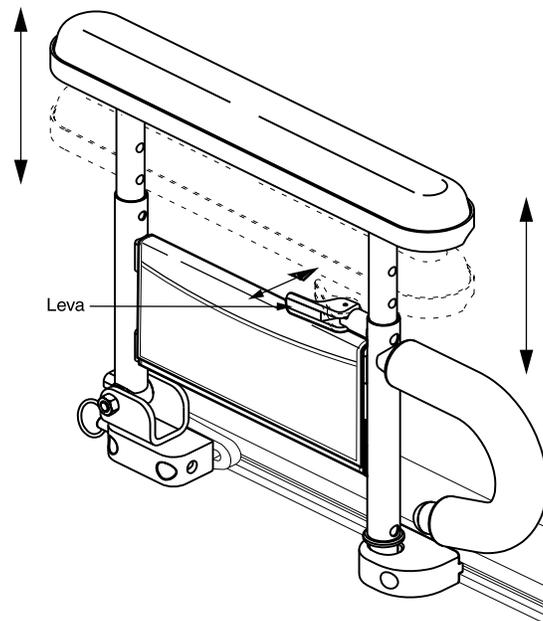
Smontaggio e montaggio bracciolo sollevabile a doppio piantone
